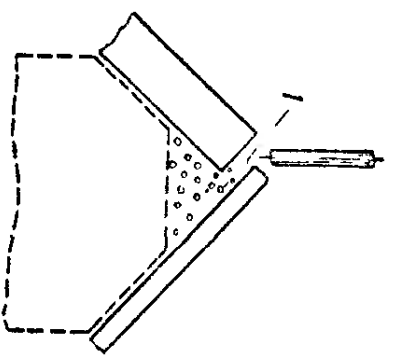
Сварка угловых швов на флюсовой подушке:
